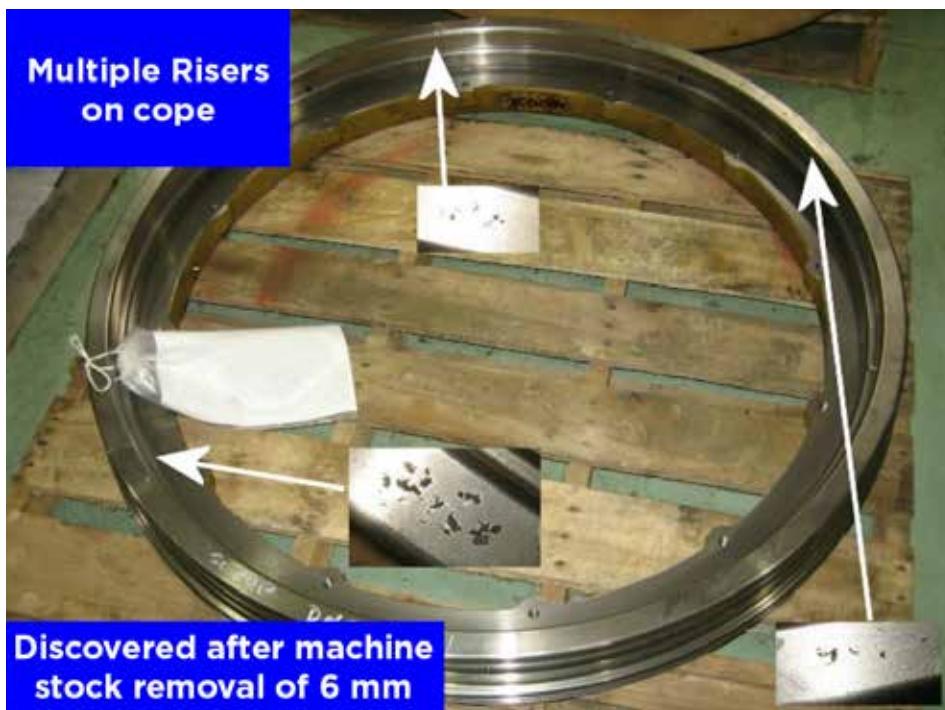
Apariencia de la Porosidad en pieza mecanizada.
